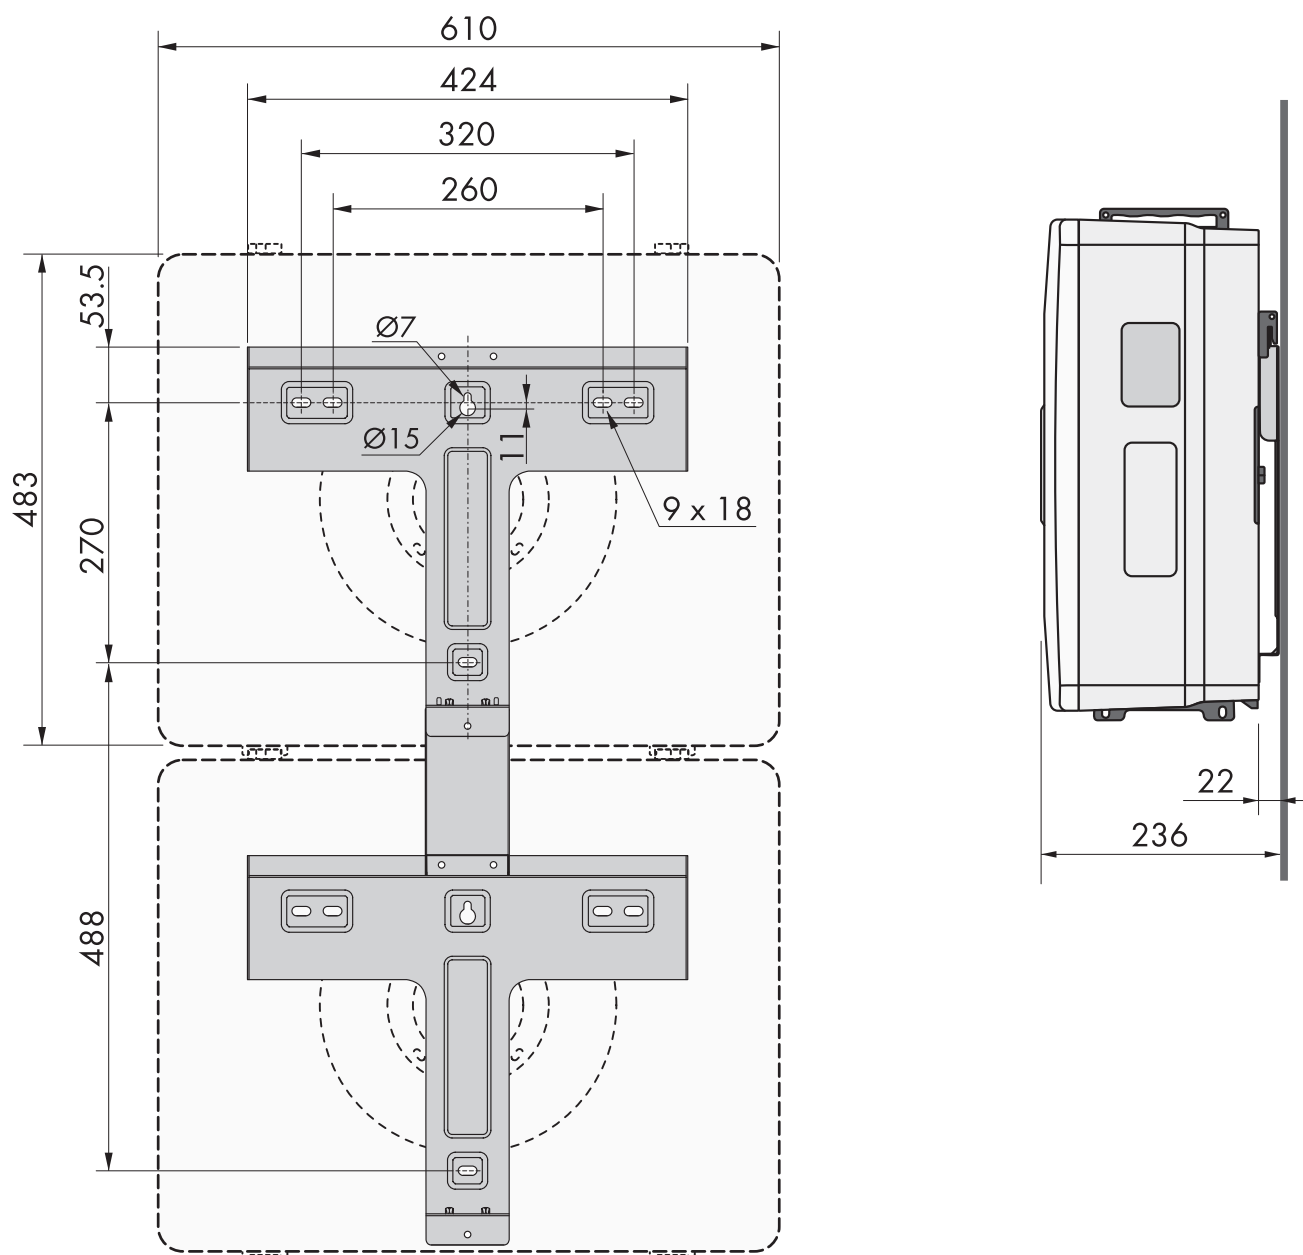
Posizione dei punti di fissaggio (misure in mm)
